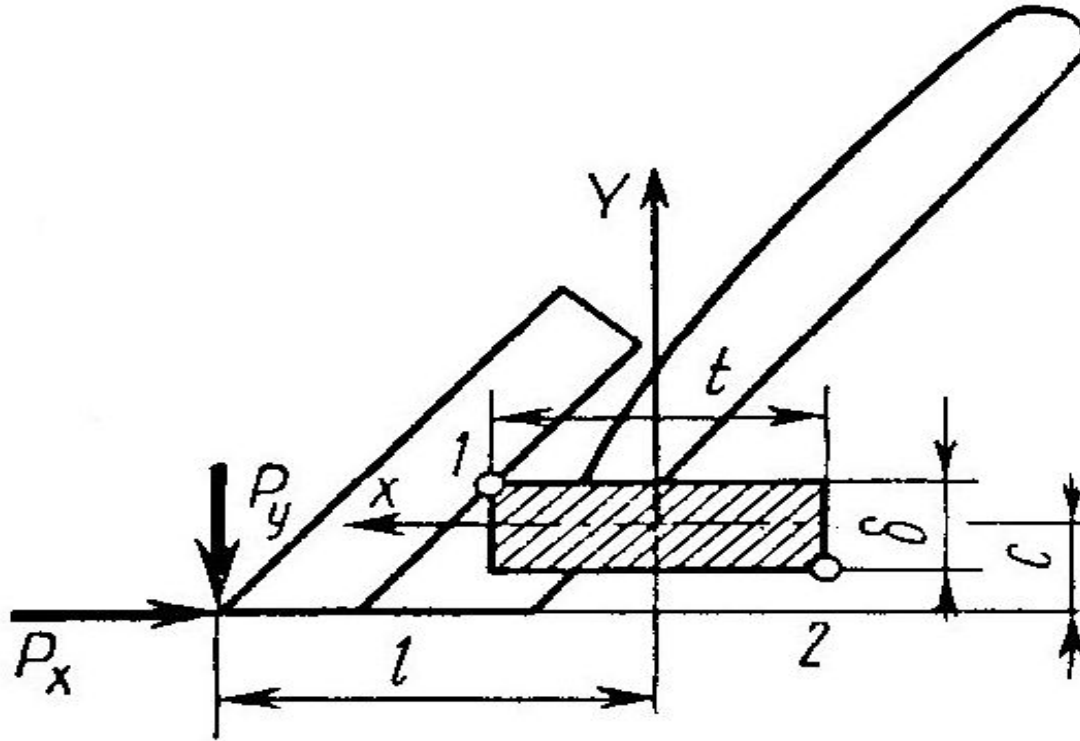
Схема к расчёту стойки корпуса в сечении 1-1
